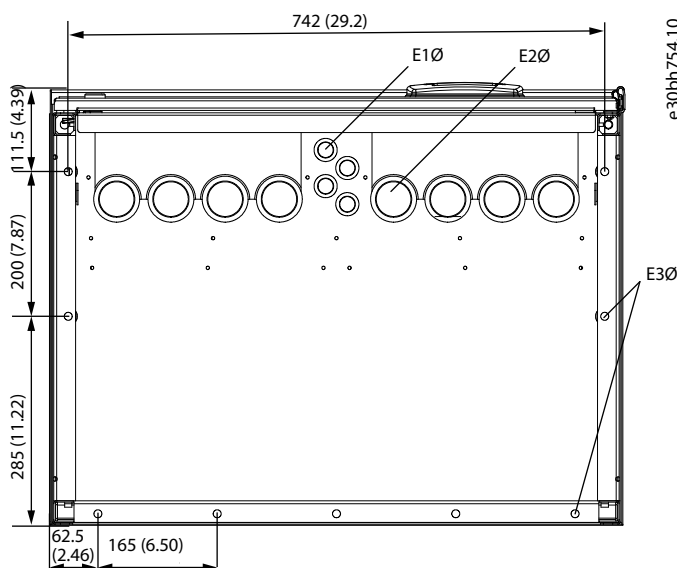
Abmessungen der Befestigungsbohrungen für VACON® NXS/NXP AC Drive, FR11 Standalone
